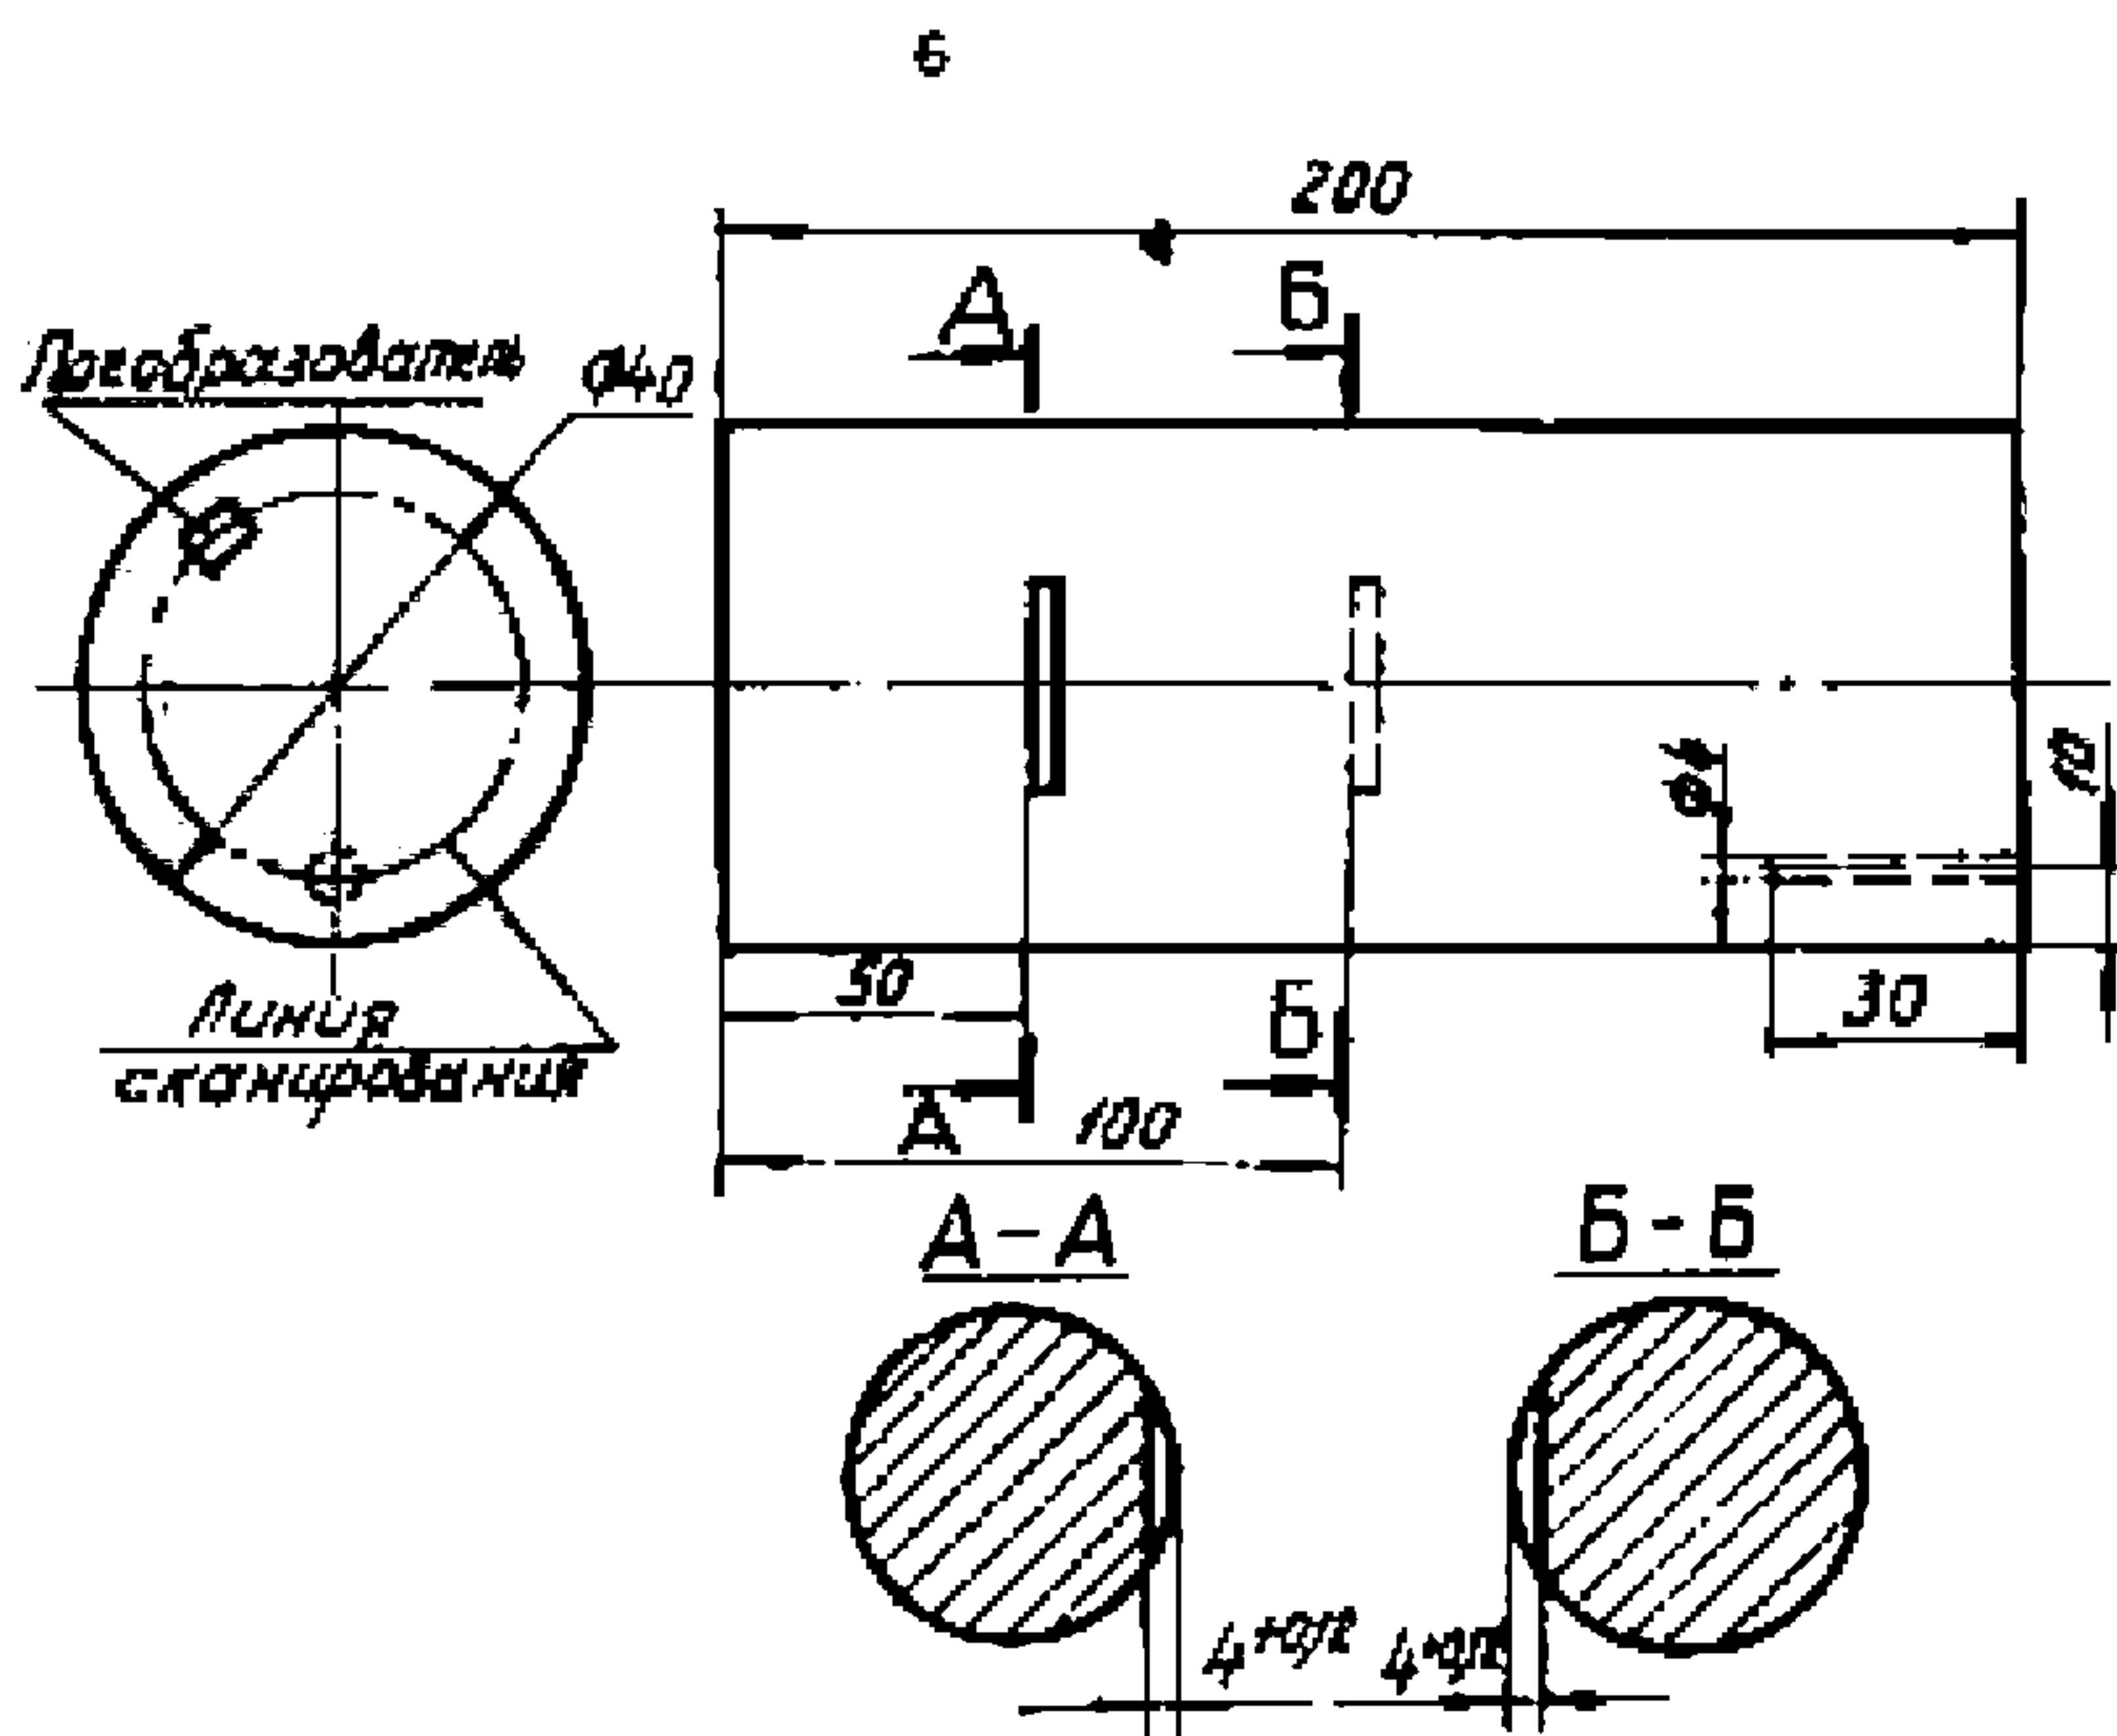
Стандартный образец для настройки ультразвукового прибора при НК элеваторов
